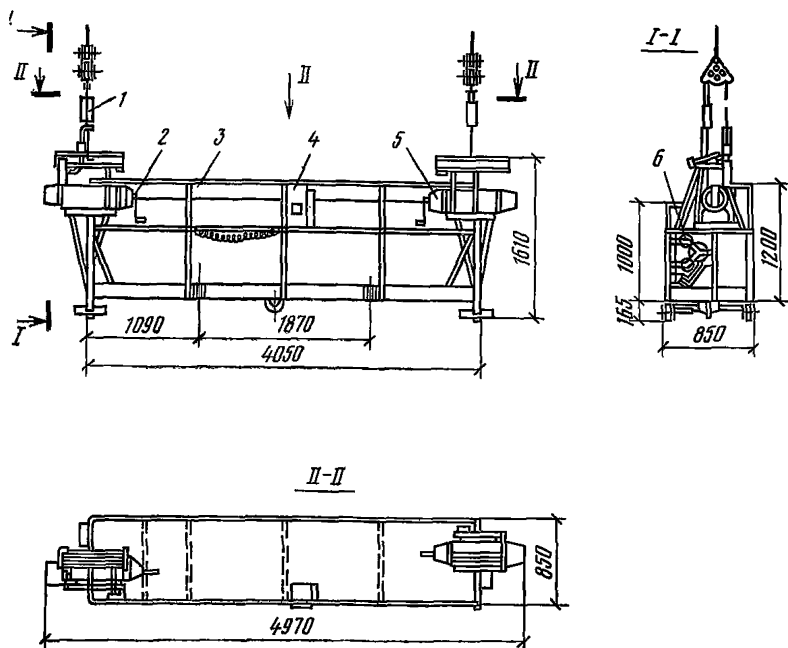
Люлька двухместная ЛЭ-30-250 конструкции СКБ Мосстроя
